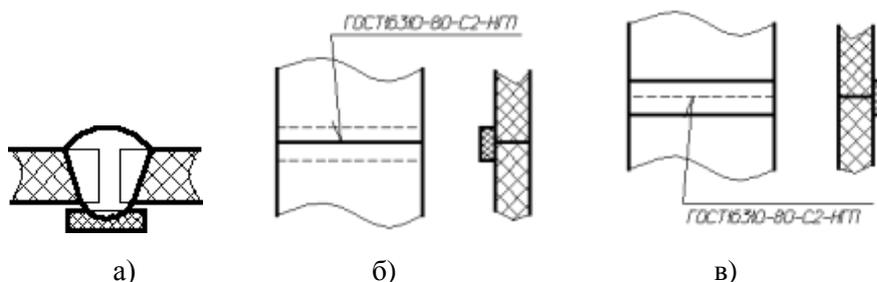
Шов стыкового соединения без скоса кромок, односторонний: а) форма поперечного сечения шва; б) с лицевой стороны; в) с оборотной стороны
